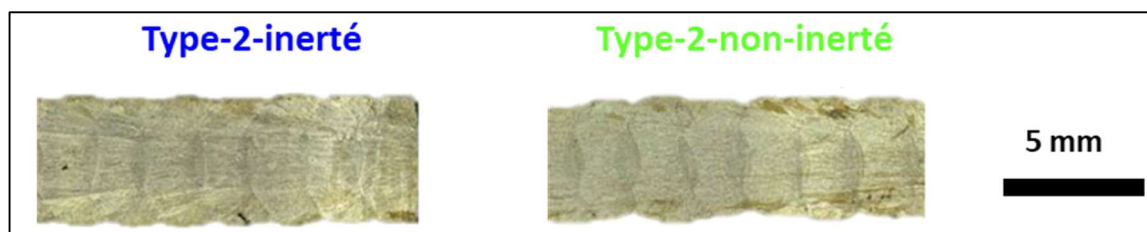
vues en coupe transversale de murs Type-P2 construits avec et sans inertage
